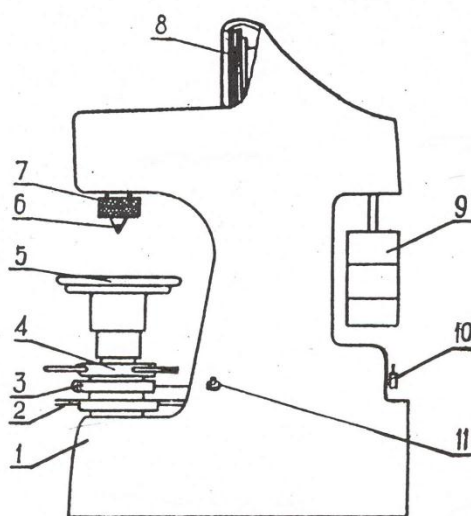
Схема твердомера Роквелла: 1 – корпус;
